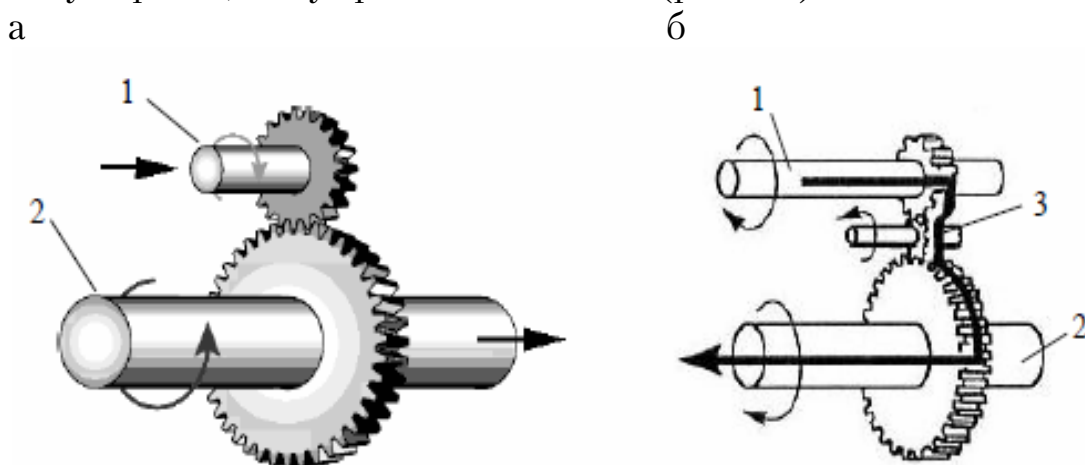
Принцип работы двухвальной коробки передач:
